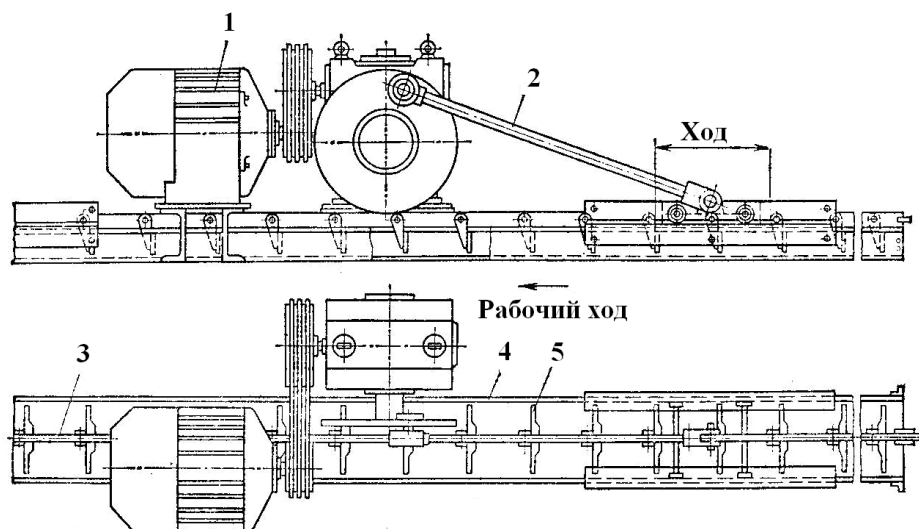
Штанговый скребковый конвейер для перемещения дробленой стружки: 1 – привод; 2 – кривошипно-шатунный механизм; 3 – штанга; 4 – желоб; 5 – скребки
